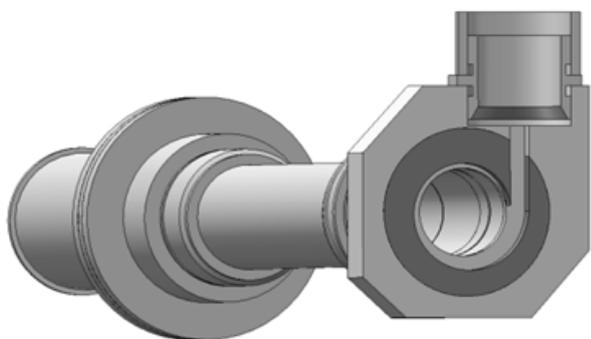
Поперечное сечение закручивающего устройства вихревой трубы
